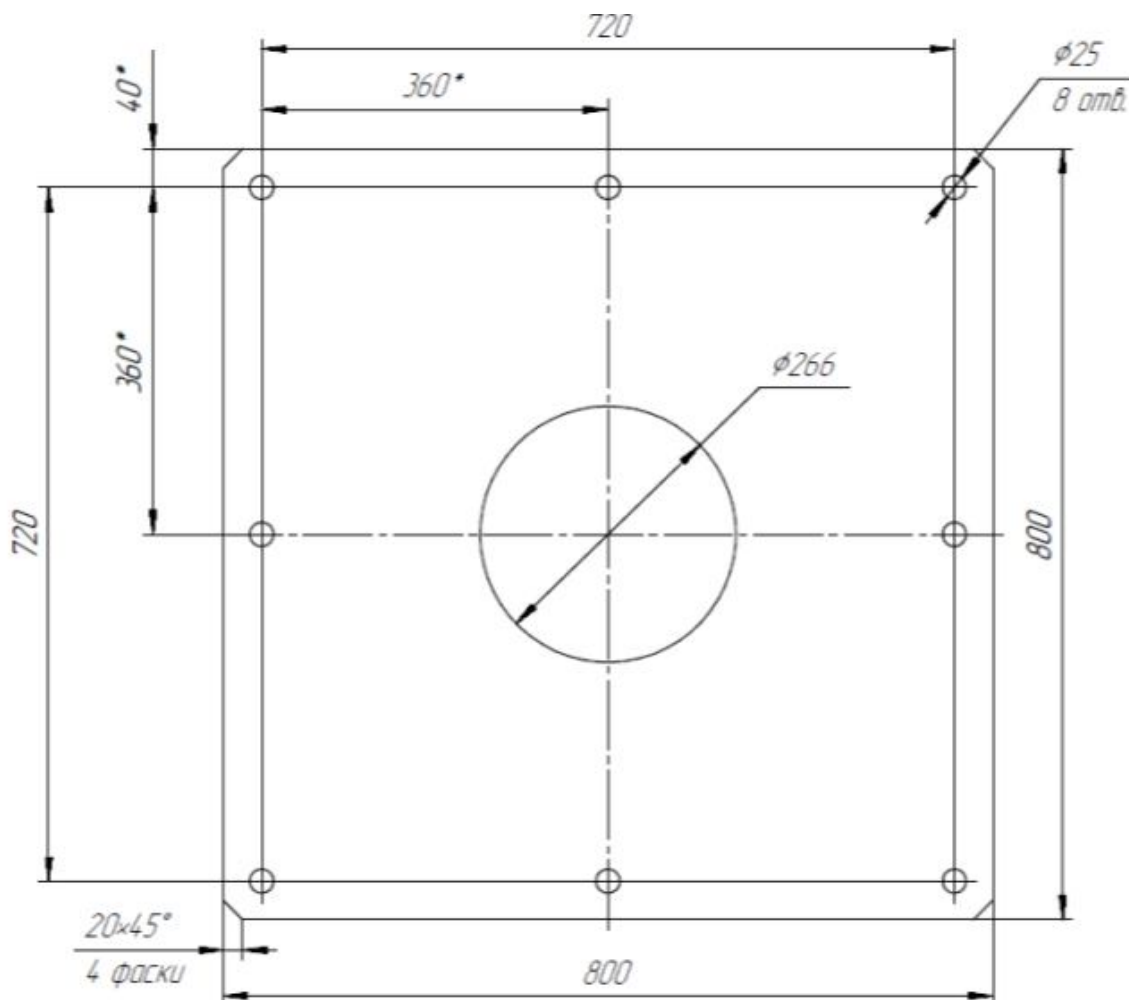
Крепление ОПУ к фундаменту/площадке
